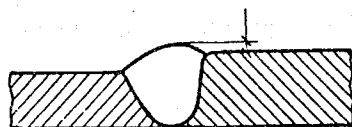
Допускаемое расположение поверхности шва при разной толщине свариваемых деталей
